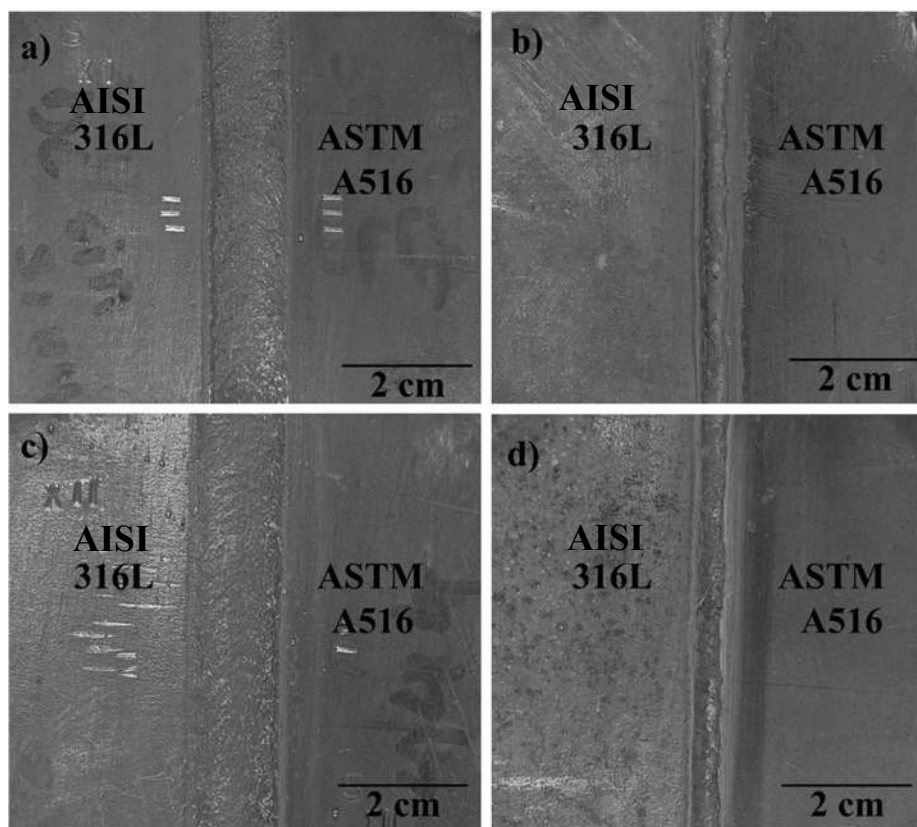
Macrografías de las soldaduras de referencia, a) corona de la soldadura en modo DC por rocío, b) raíz de la soldadura en modo DC por rocío, c) corona soldadura en modo DC-Pulsada y d) raíz soldadura en modo DC-Pulsada.
